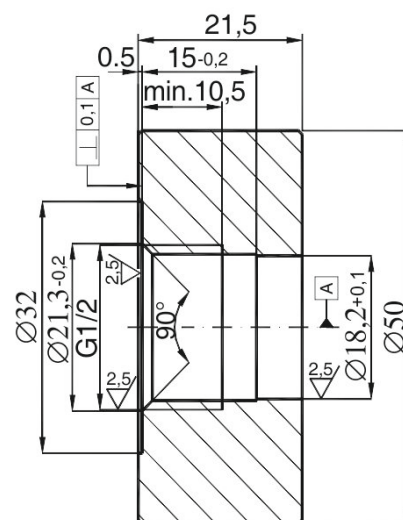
д. Монтажное кольцо под сварку для присоединения CG1/2
